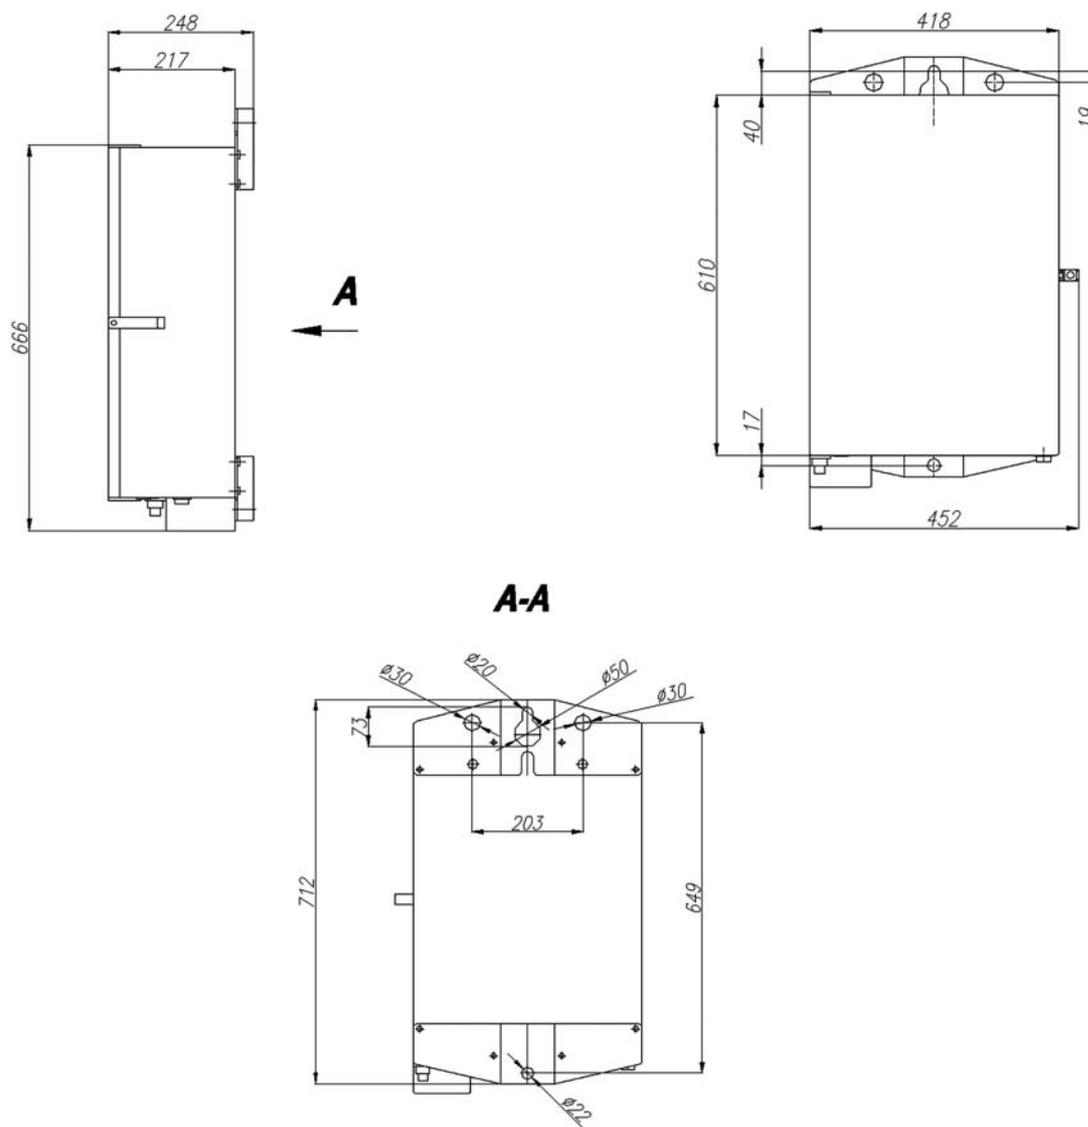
Габаритные и присоединительные размеры RC/TEL
